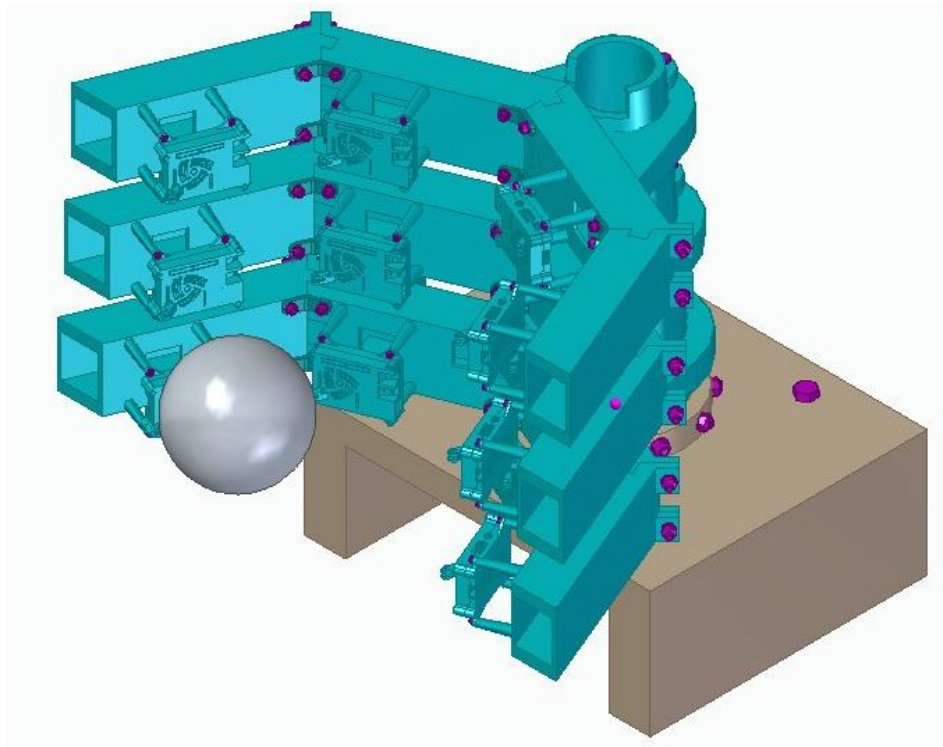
Vista en 3D de la solución propuesta para la estructura. Se aprecia la posición de la cabeza del sujeto respecto a la estructura.
